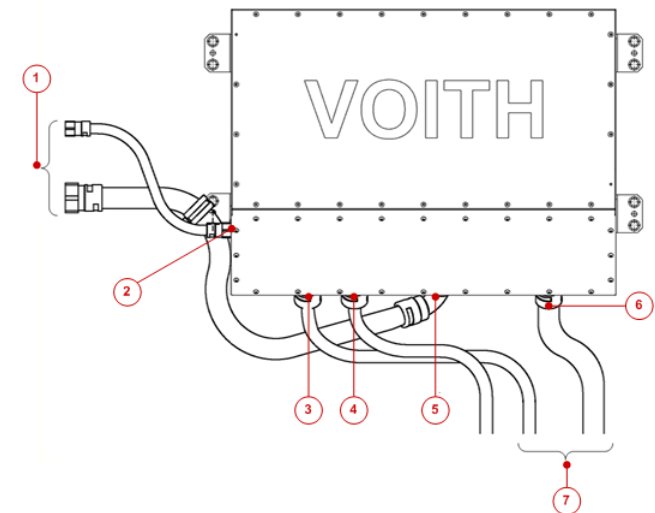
Kabeldurchführungen am Gehäuse / Cable bushings at housing
